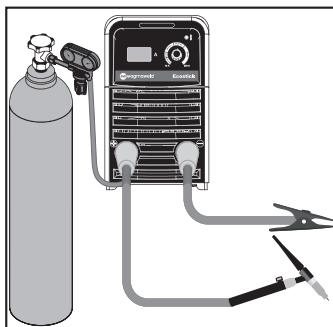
Подсоединения для TIG-сварки
